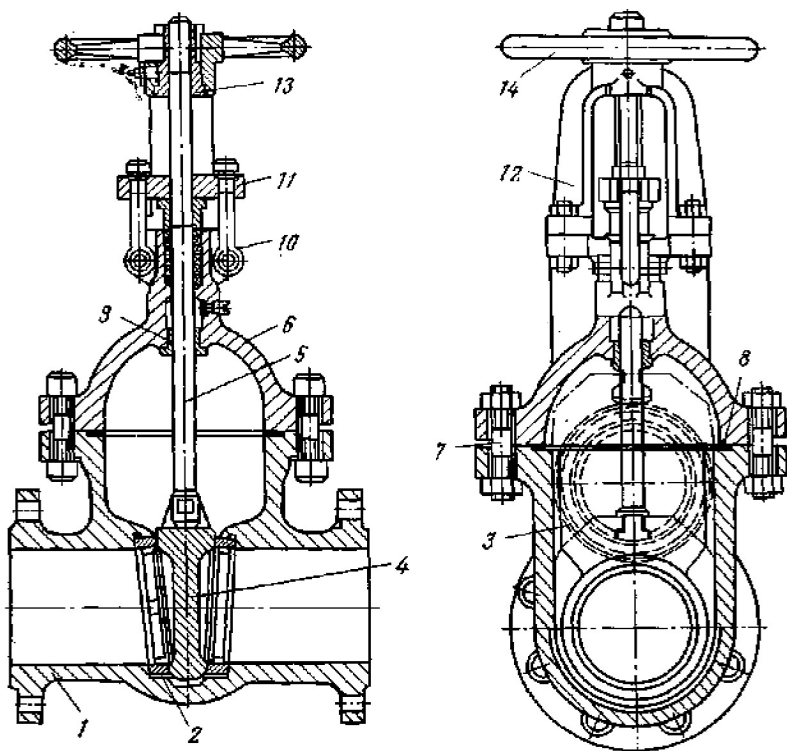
Полнопроходная задвижка с цельным клином:
